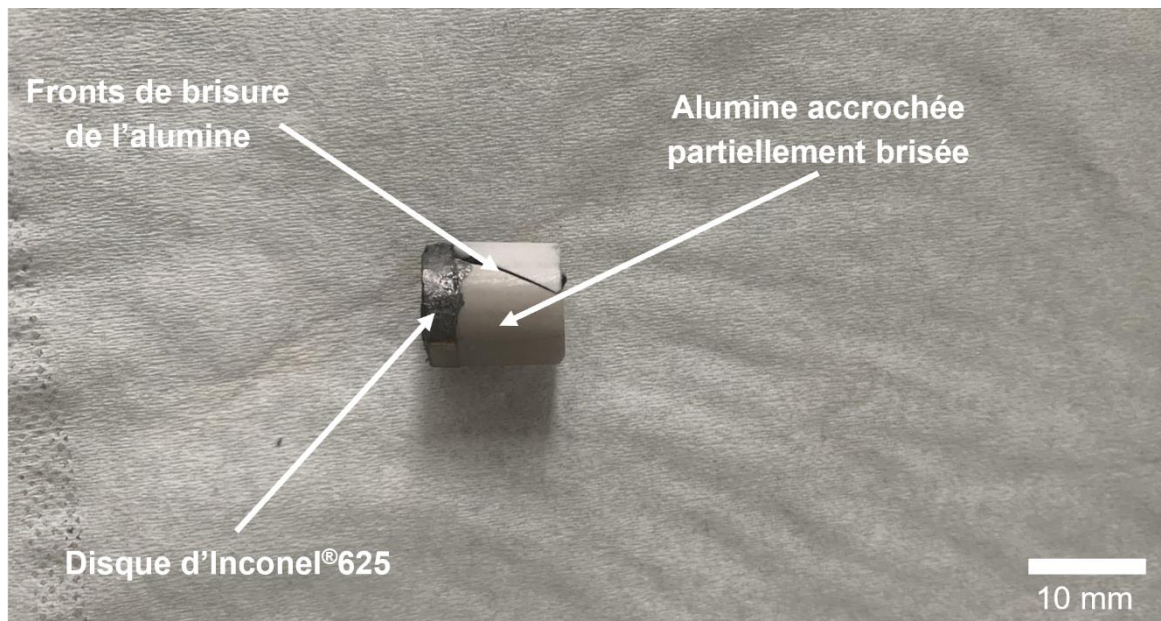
Assemblage Inconel®625-Alumine après thermocompression pendant 3 h à 1150 °C
